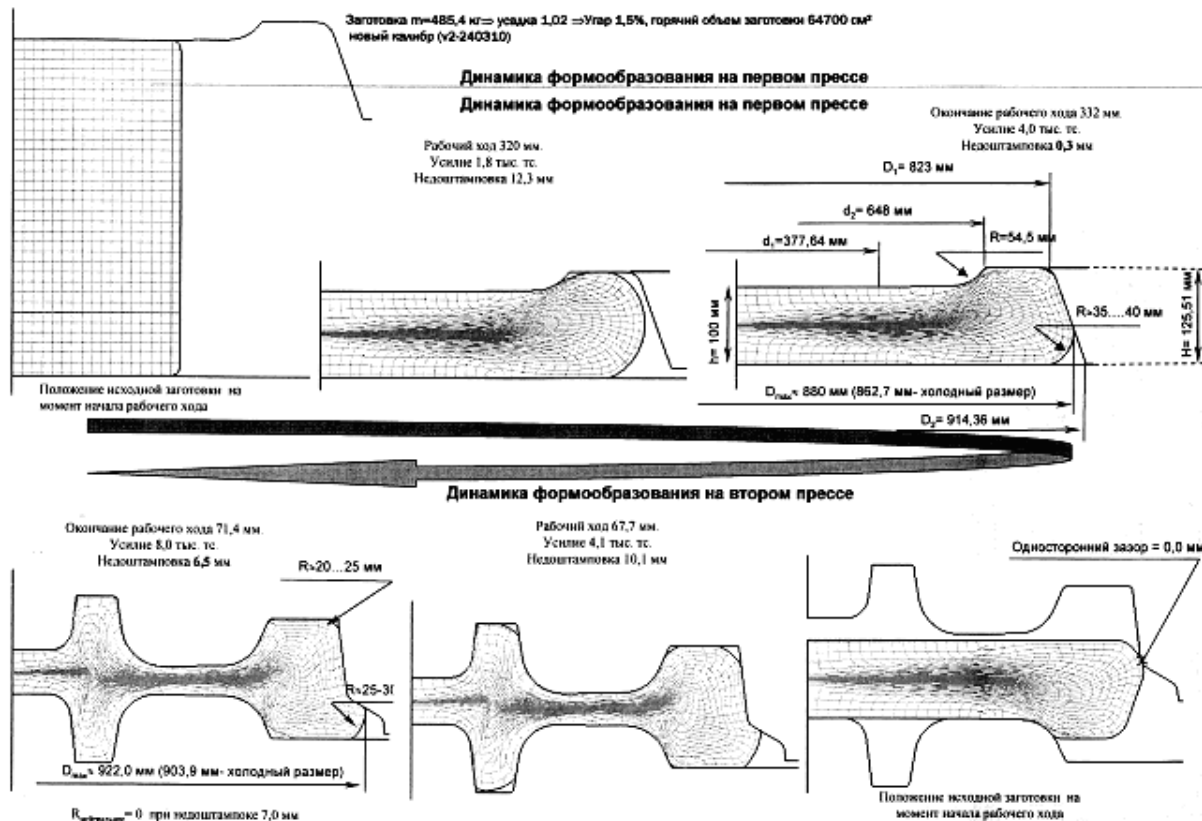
Анализ процесса формообразования заготовки колеса под раскатку
